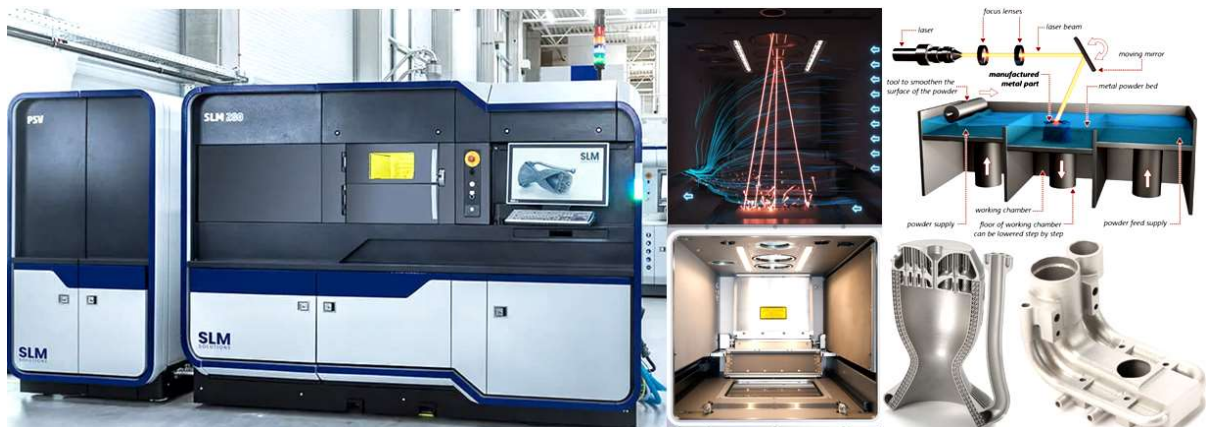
Metal 3D Printer SLM 280 PS, його робоча камера і вироби
